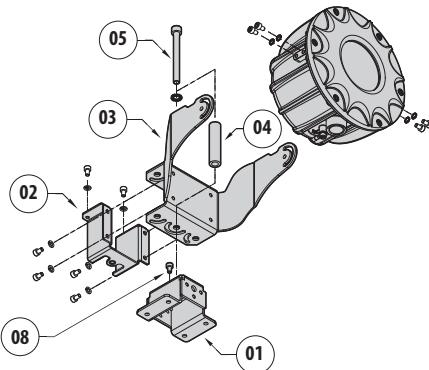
Fixação em parapeito com entrada de cabos por baixo.
